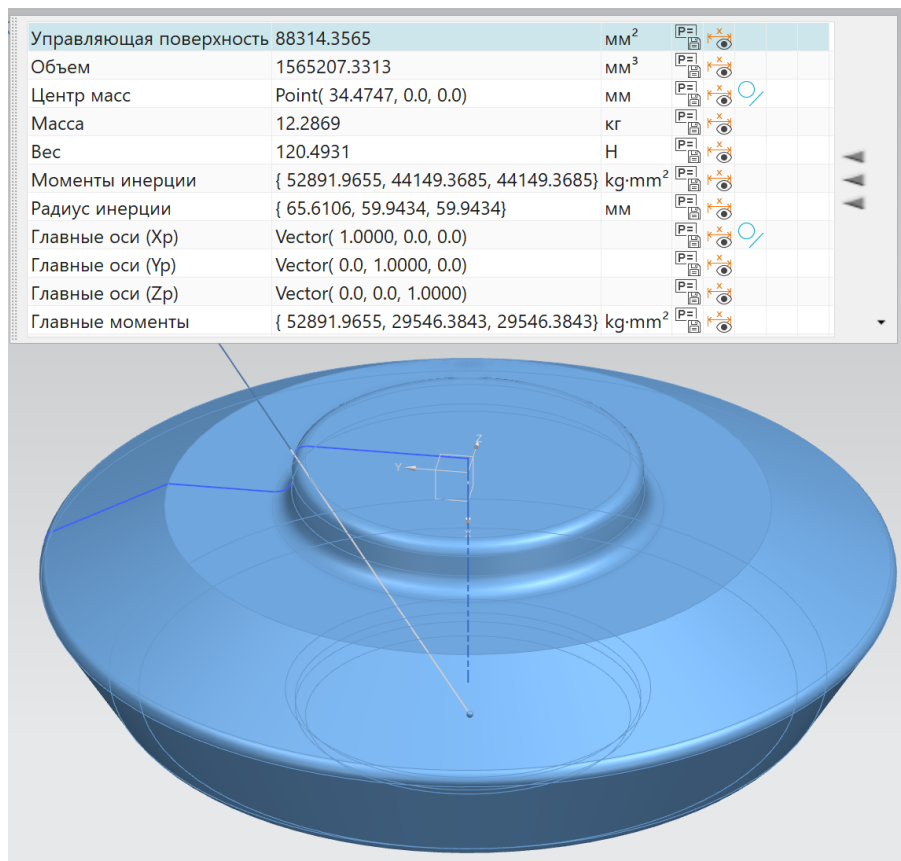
Модель штампованої заготовки на ГKM
